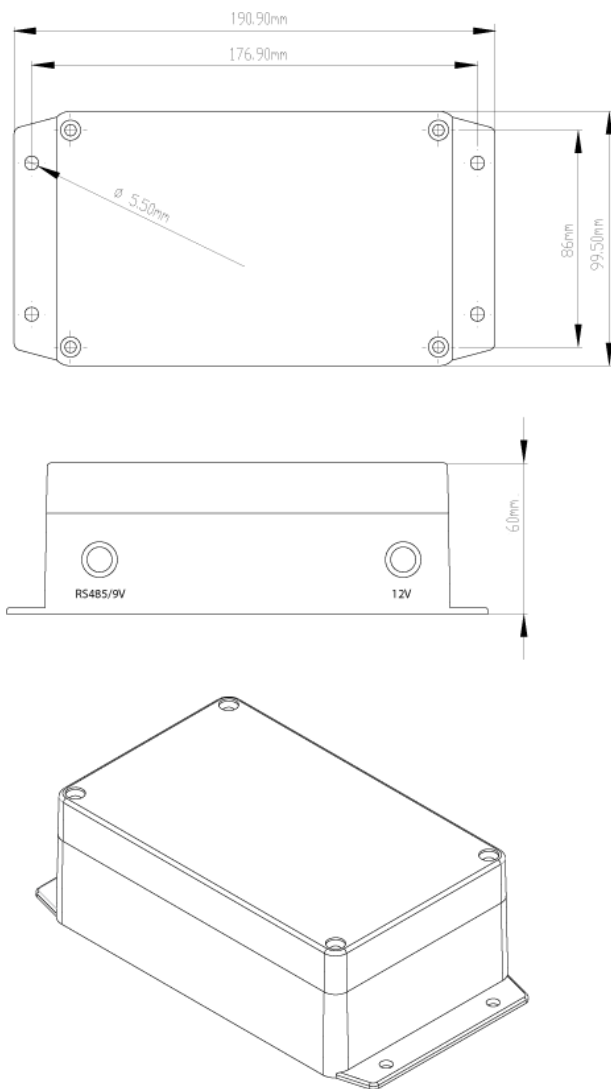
Внешний вид, габаритные и крепежные размеры блока.
